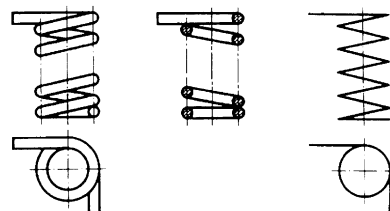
Zylindrische Schrauben-Drehfeder (Schenkelfeder) aus Draht mit rundem Querschnitt (Wickelrichtung rechts) (DIN 2088)
